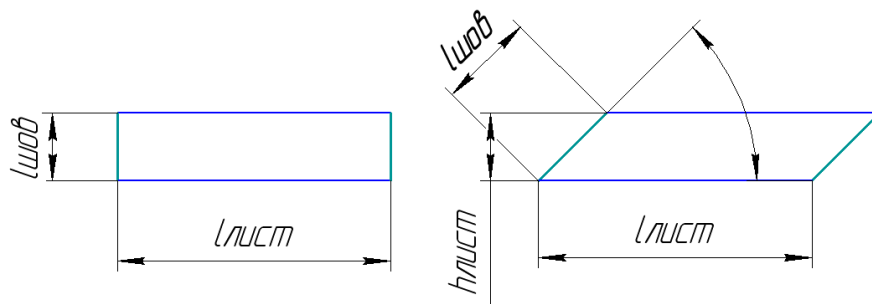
Расчетные размеры прямоугольного и косоугольного листа
